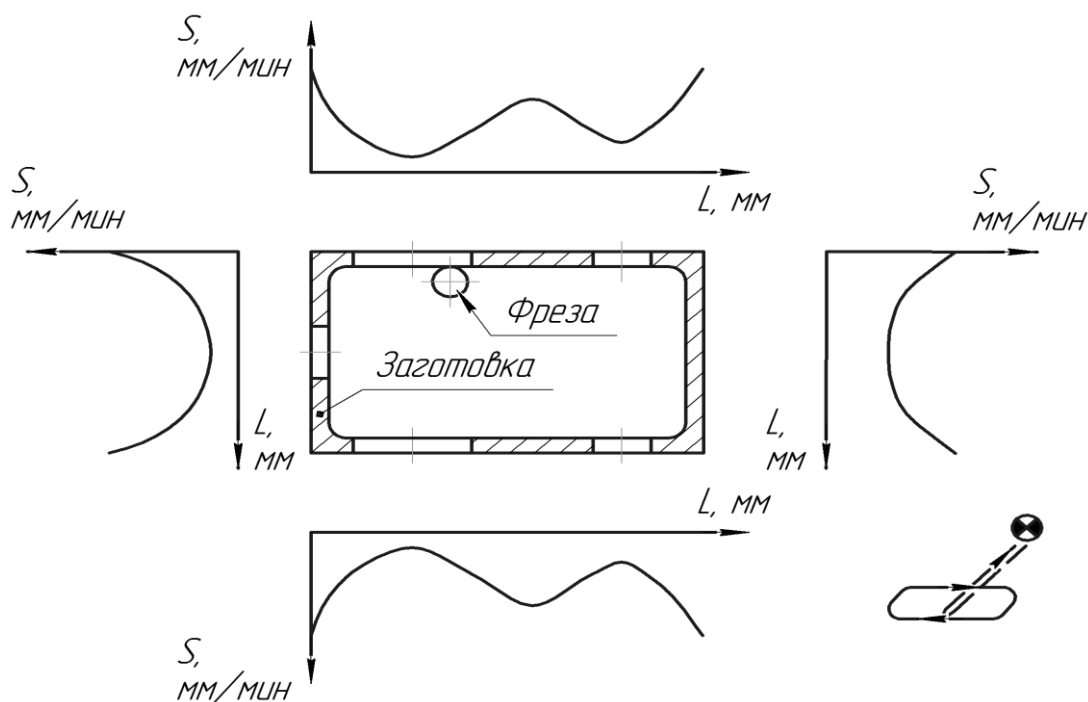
Способ управления показателями точности фрезерования нежесткой детали
